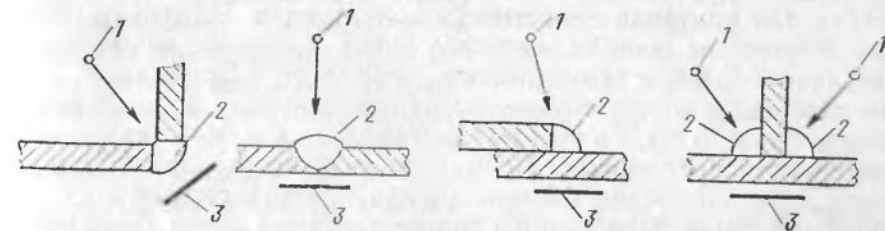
Схемы просвечивания сварных швов
